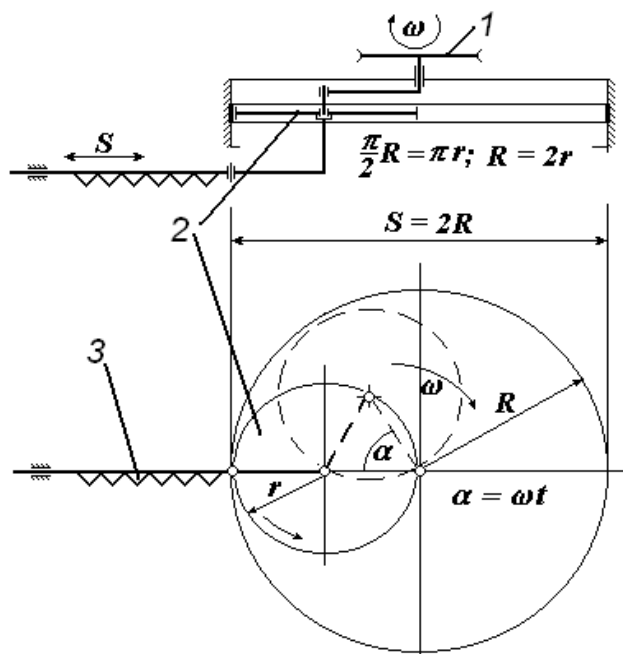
Планетарный механизм Шумахера для привода режущего аппарата
